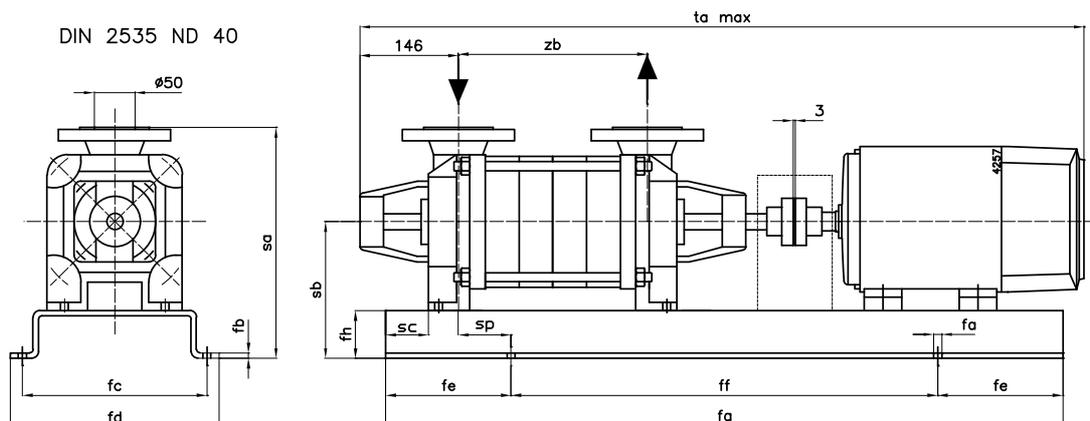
Габаритный чертеж агрегата MCHZ(S) 14a.
